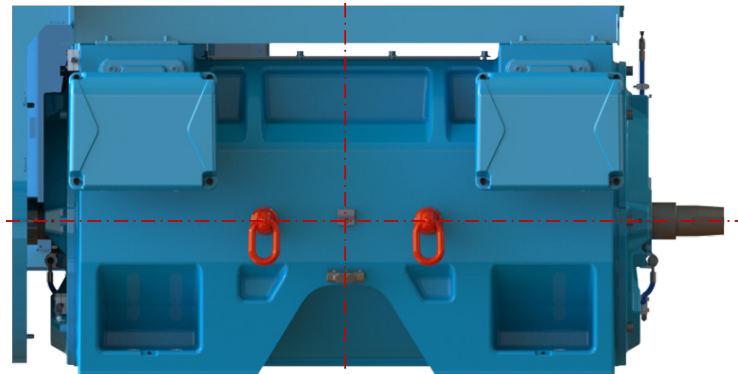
Detalhe da posição para fixação do dispositivo do sistema WEG Motor Scan nos motores W60
